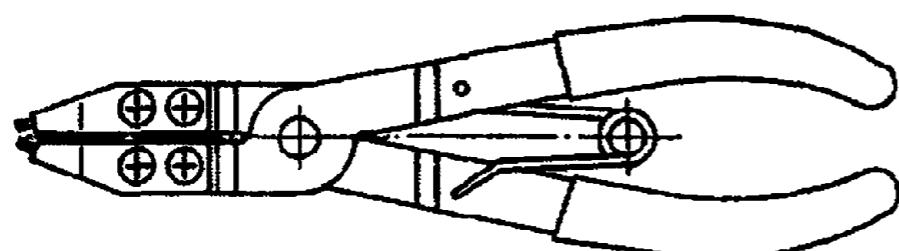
Спецпассатижи для снятия и установки внутренних упорных колец
